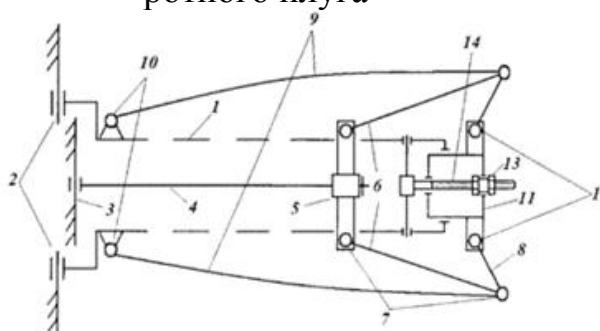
Конструктивная схема механизма предварительной нагрузки секции плуга (патент РФ № 2701690)
